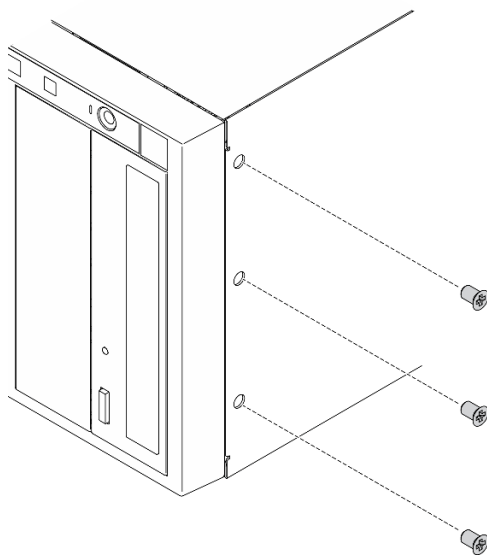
Rimozione delle viti sulla parte superiore dello chassis
